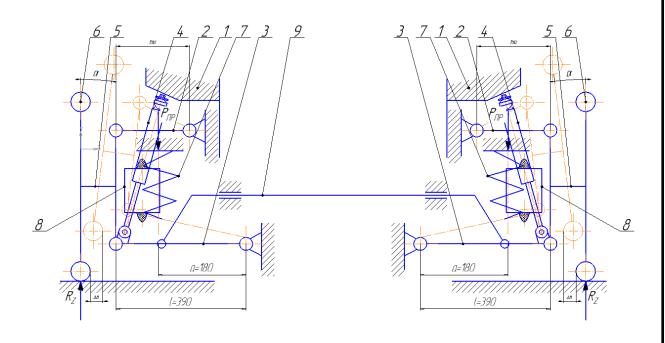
Кинематическая схема разрабатываемой задней независимой подвески на двойных поперечных рычагах: 1 - кузов автомобиля; 2 - верхние рычаги; 3 - нижние рычаги; 4 - амортизаторы; 5 - ступицы колёс; 6 - колёса; 7 - пружины; 8 - буферы отбоя; 9 - стабилизатор поперечной устойчивости
